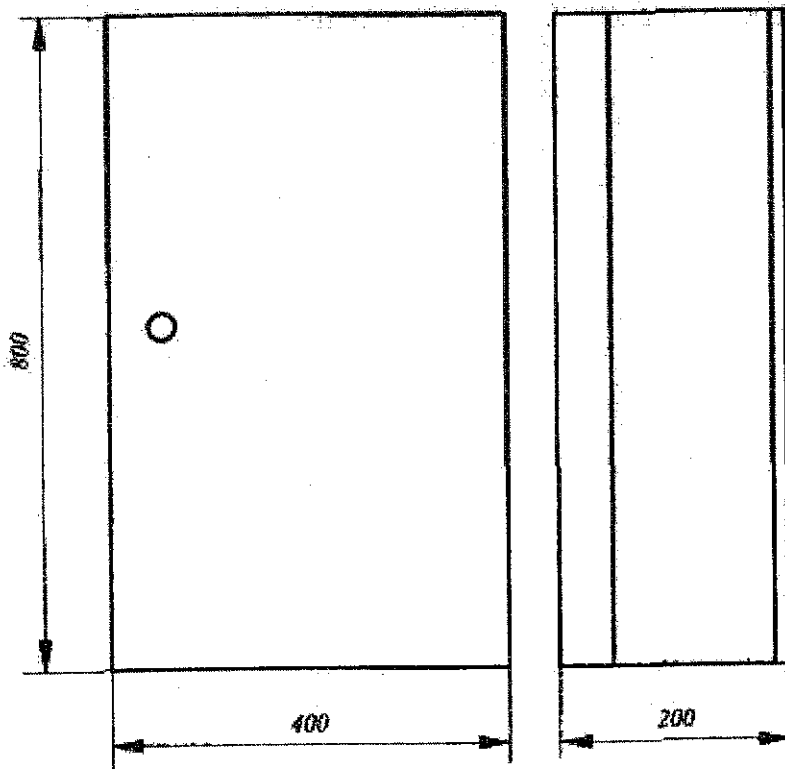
Габаритные размеры щитка коттеджного ЯВУ-03К-80-У3
